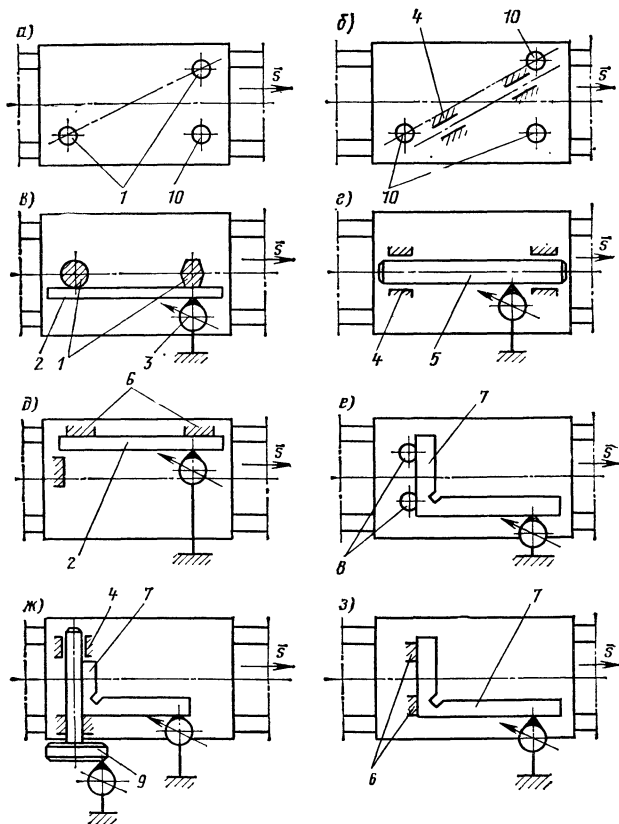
Типовые схемы контроля точности компонентов приспособлений с узлами прямолинейного перемещения:
